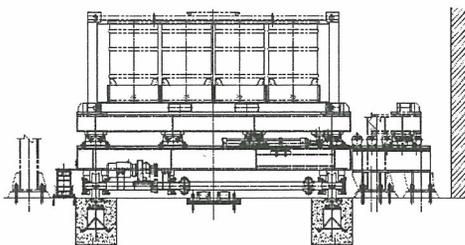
운반용기 출입용 Slider 및 Jig.
